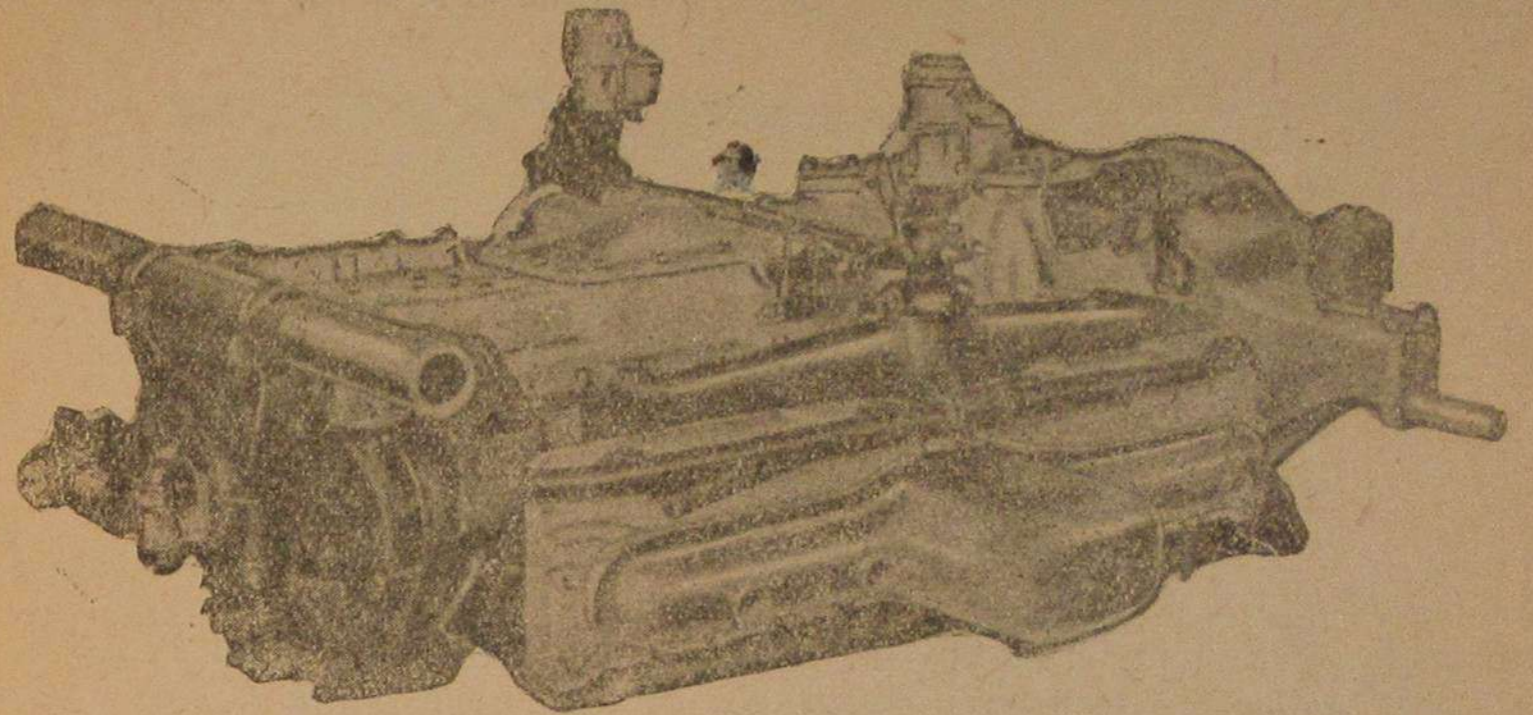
Двигатель Уайт-10А двенадцатицилиндровый с горизонтальным расположением цилиндров; вид спереди.
